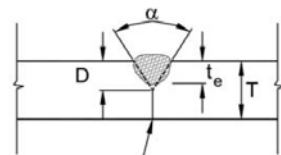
Dimensión efectiva de las soldaduras a tope con penetración completa. Extraída de los comentarios CIRSOC 301/05
